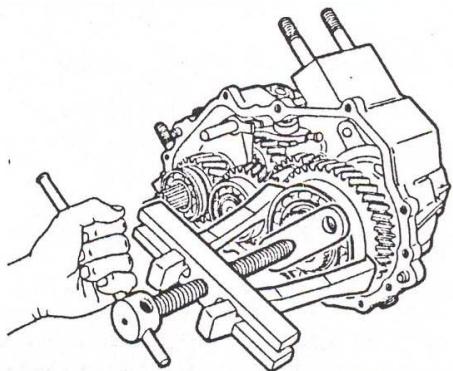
Спрессовка подшипника с шестерней дифференциала
